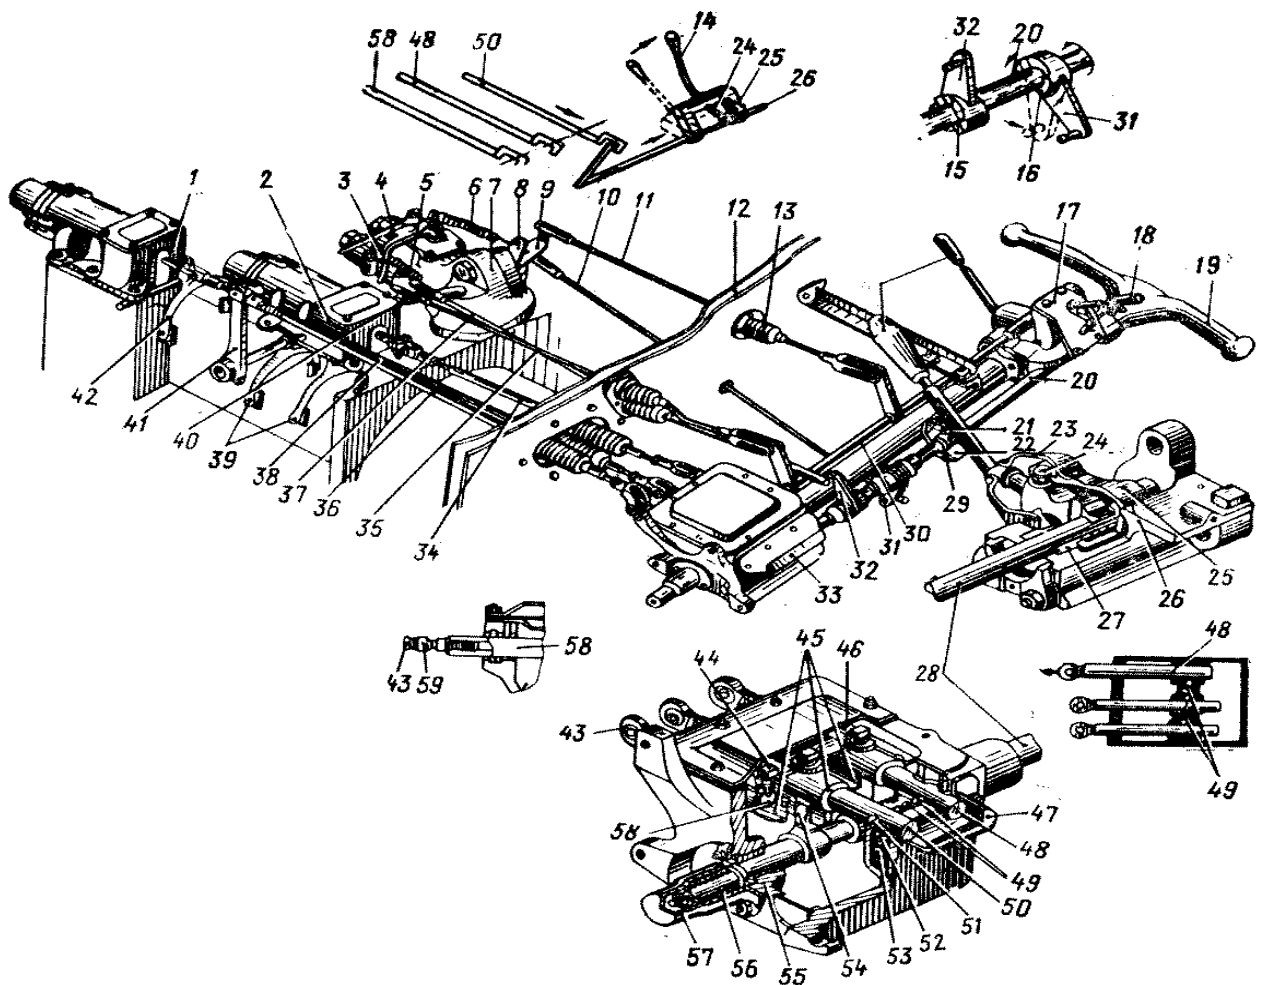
Приводи управління коробкою передач і планетарними механізмами повороту
